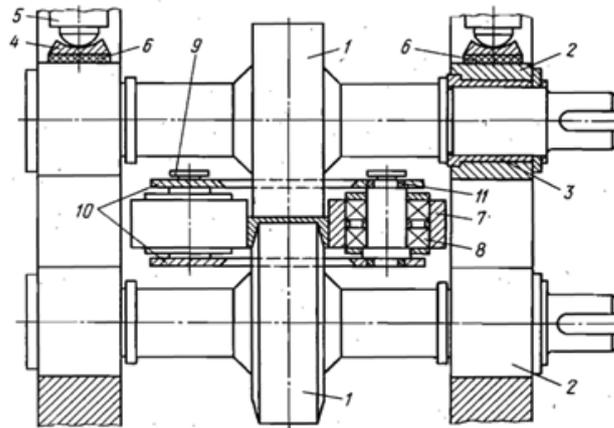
Упругий четырёхвалковый швеллерно-гибочный калибр: 1 – горизонтальный валок; 2 – подушка; 3 – подшипник; 4 – подпятник; 5 – винт; 6 – упругий элемент; 7 – вертикальный валок; 8 – подшипник; 9 – эксцентриковое нажимное устройство; 10 – опорная плита; 11 – упругий элемент
